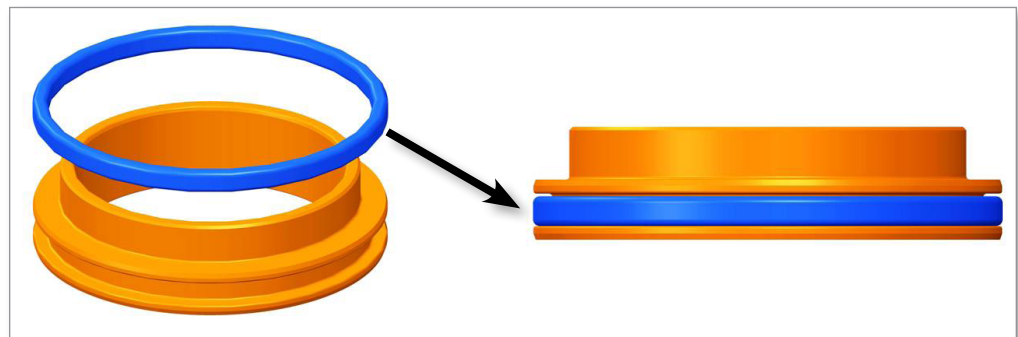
Installation der O-Ringe auf dem Kolbenboden
